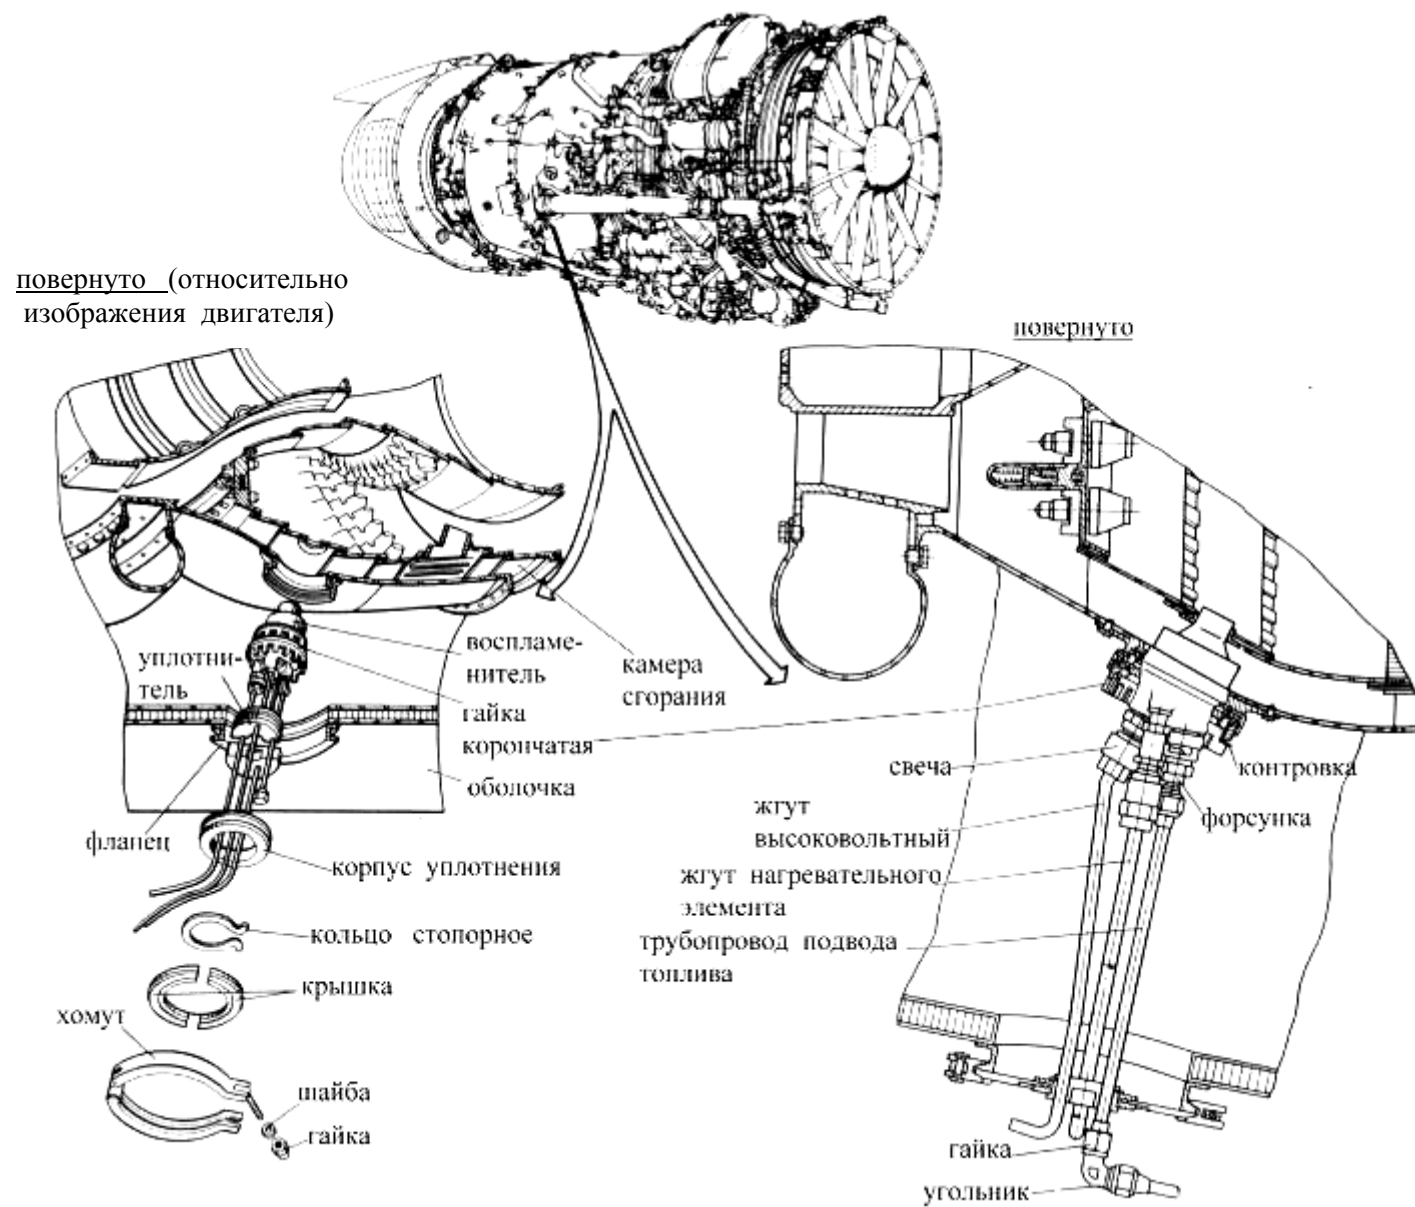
Детали крепежа и схема установки воспламенителя двигателя НК-86
